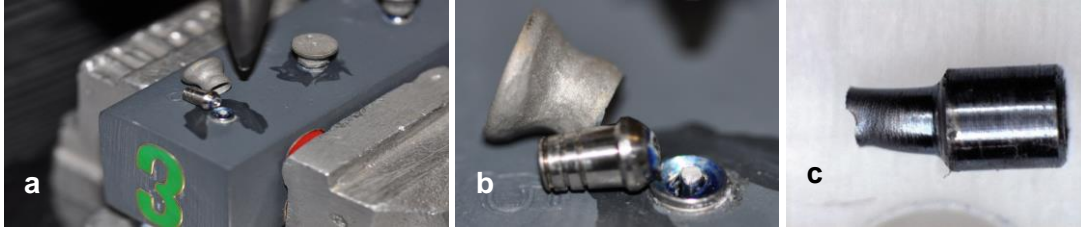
a) Fractura del sistema; b) Vista Macro; c) Tornillo deformado.
